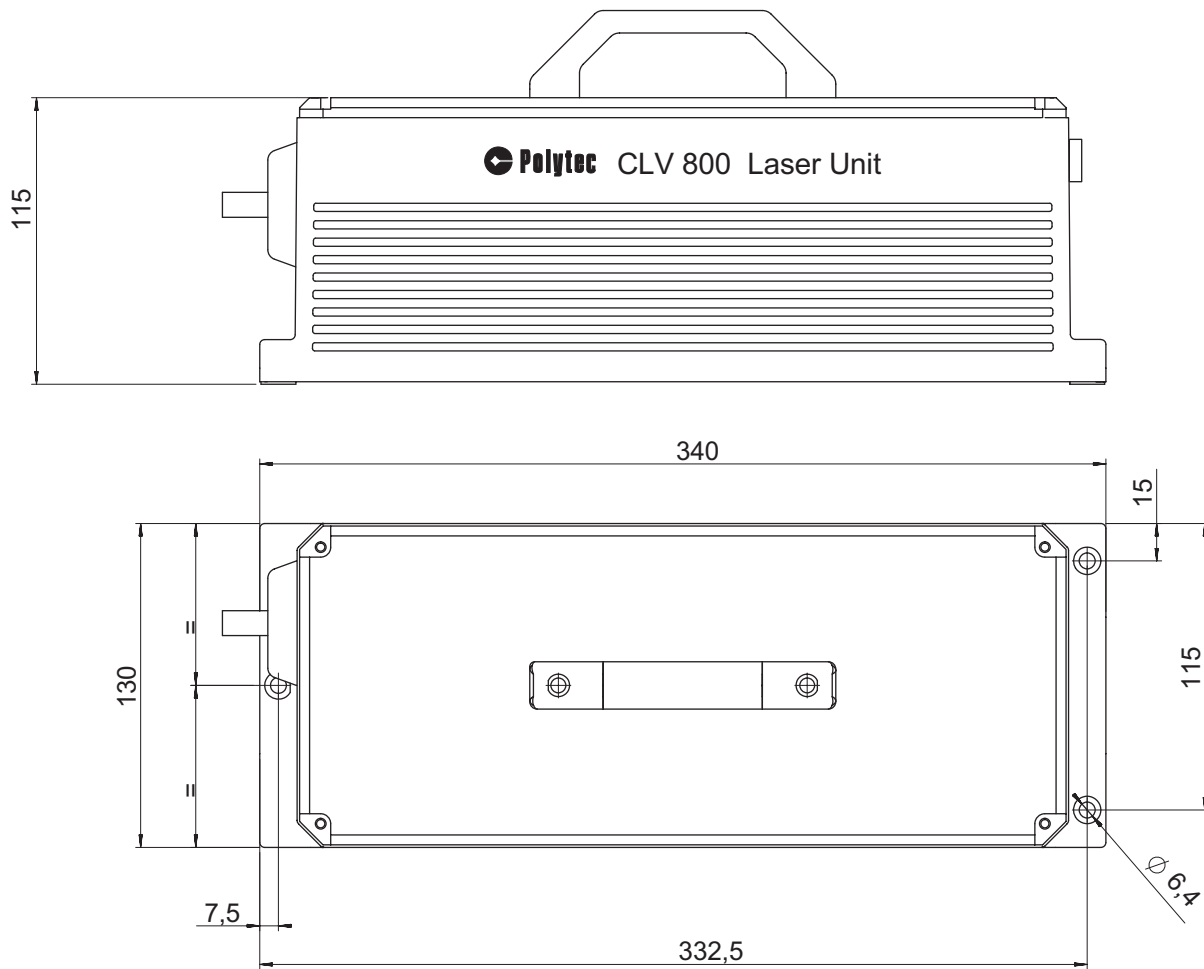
Seitenansicht und Draufsicht des externen Lasermoduls CLV-800. Die Maße sind in mm angegeben.
